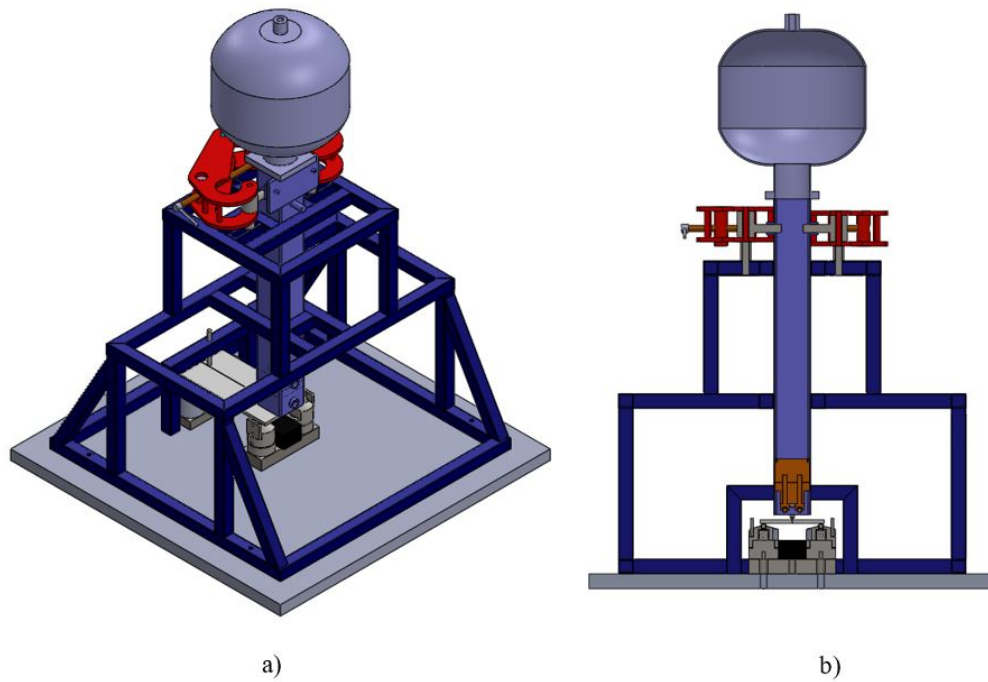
CAD de la máquina HSDT con los cinco módulos ensamblados: a) vista isométrica y b) corte transversal vertical para visualizar el proyectil.
